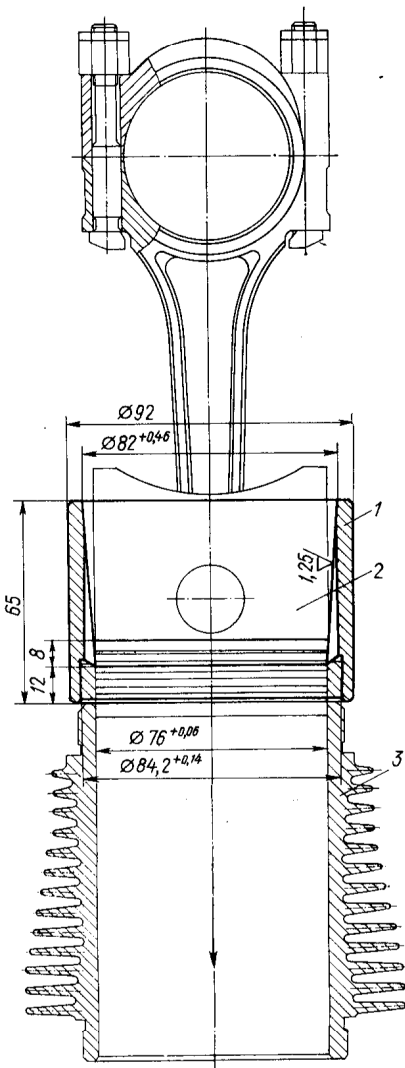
Оправка для установки поршня с кольцами в цилиндр:
